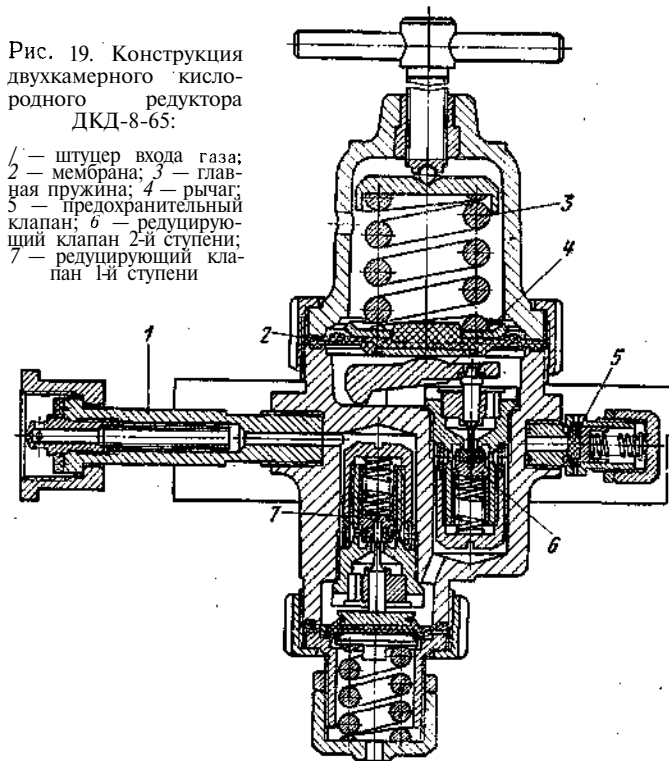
Конструкция двухкамерного кислородного редуктора ДКД-8-65:
